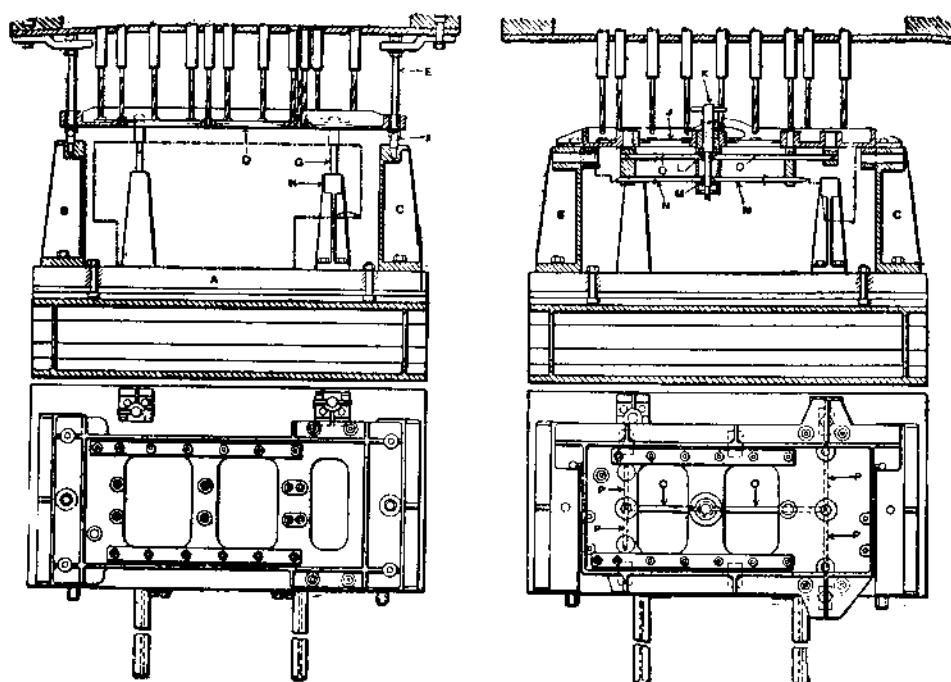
Приспособление для сверления блока и поддона Хотчкисс.
